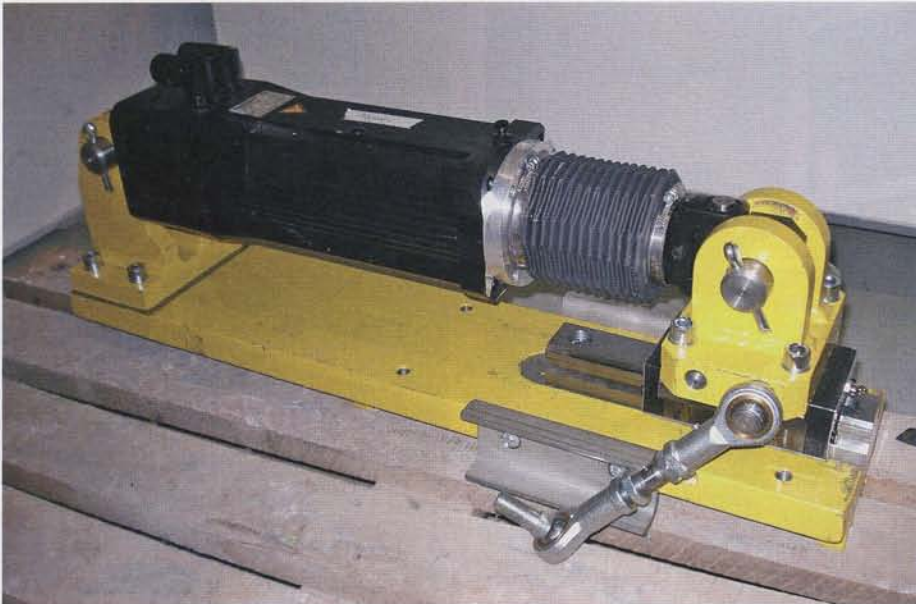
Lenkantrieb vor dem Einbau in den Kran
